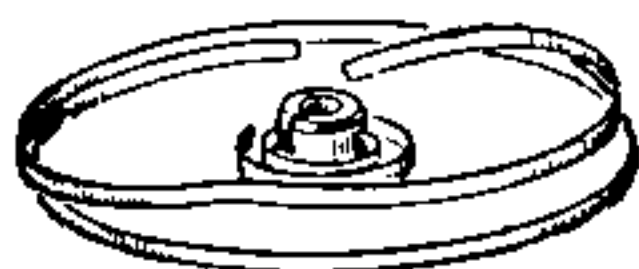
Spirale pronta per fare la spira superiore parallela al suo piano principale.
